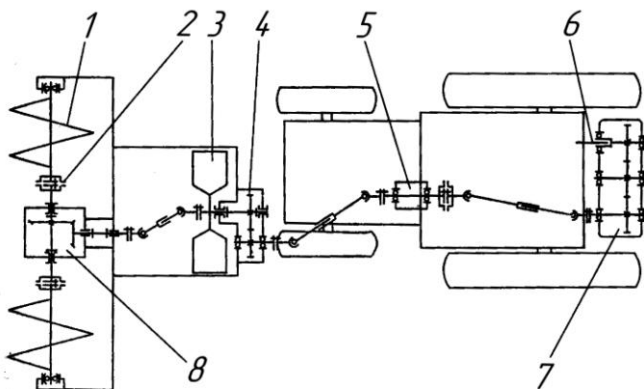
Кинематическая схема механического привода рабочего органа фрезерно-роторного снегоочистителя:
